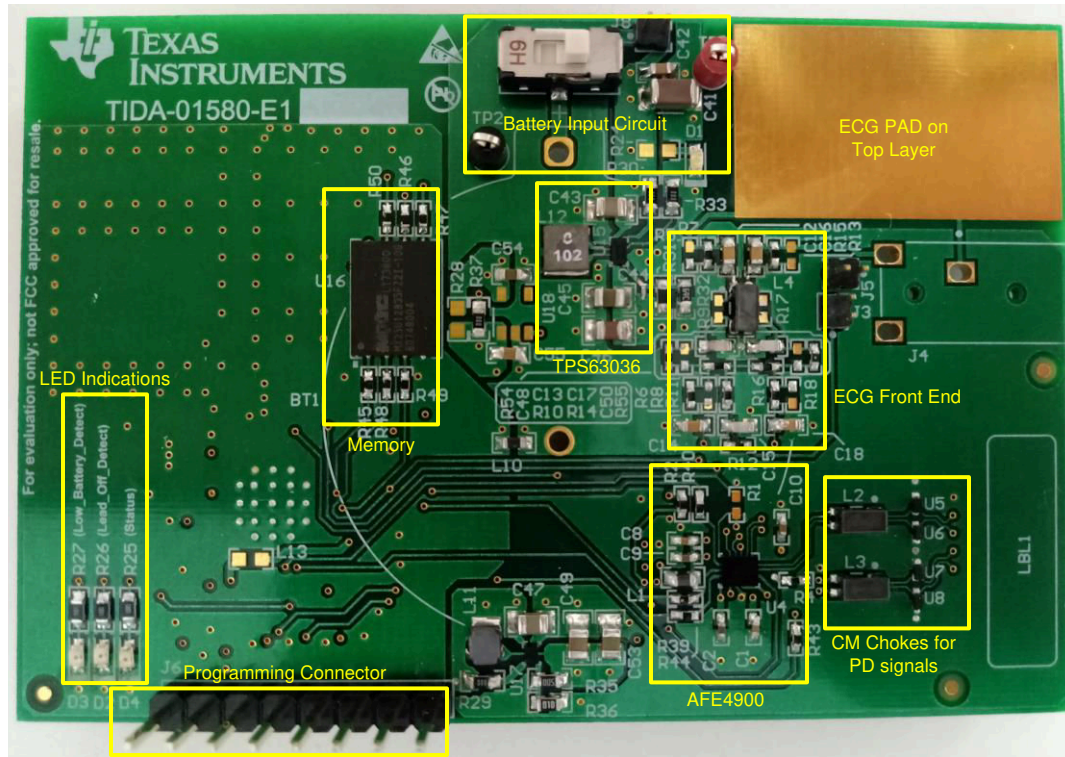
TIDA-01580 PCB - 俯视图，未安装电池座 (BT1)
